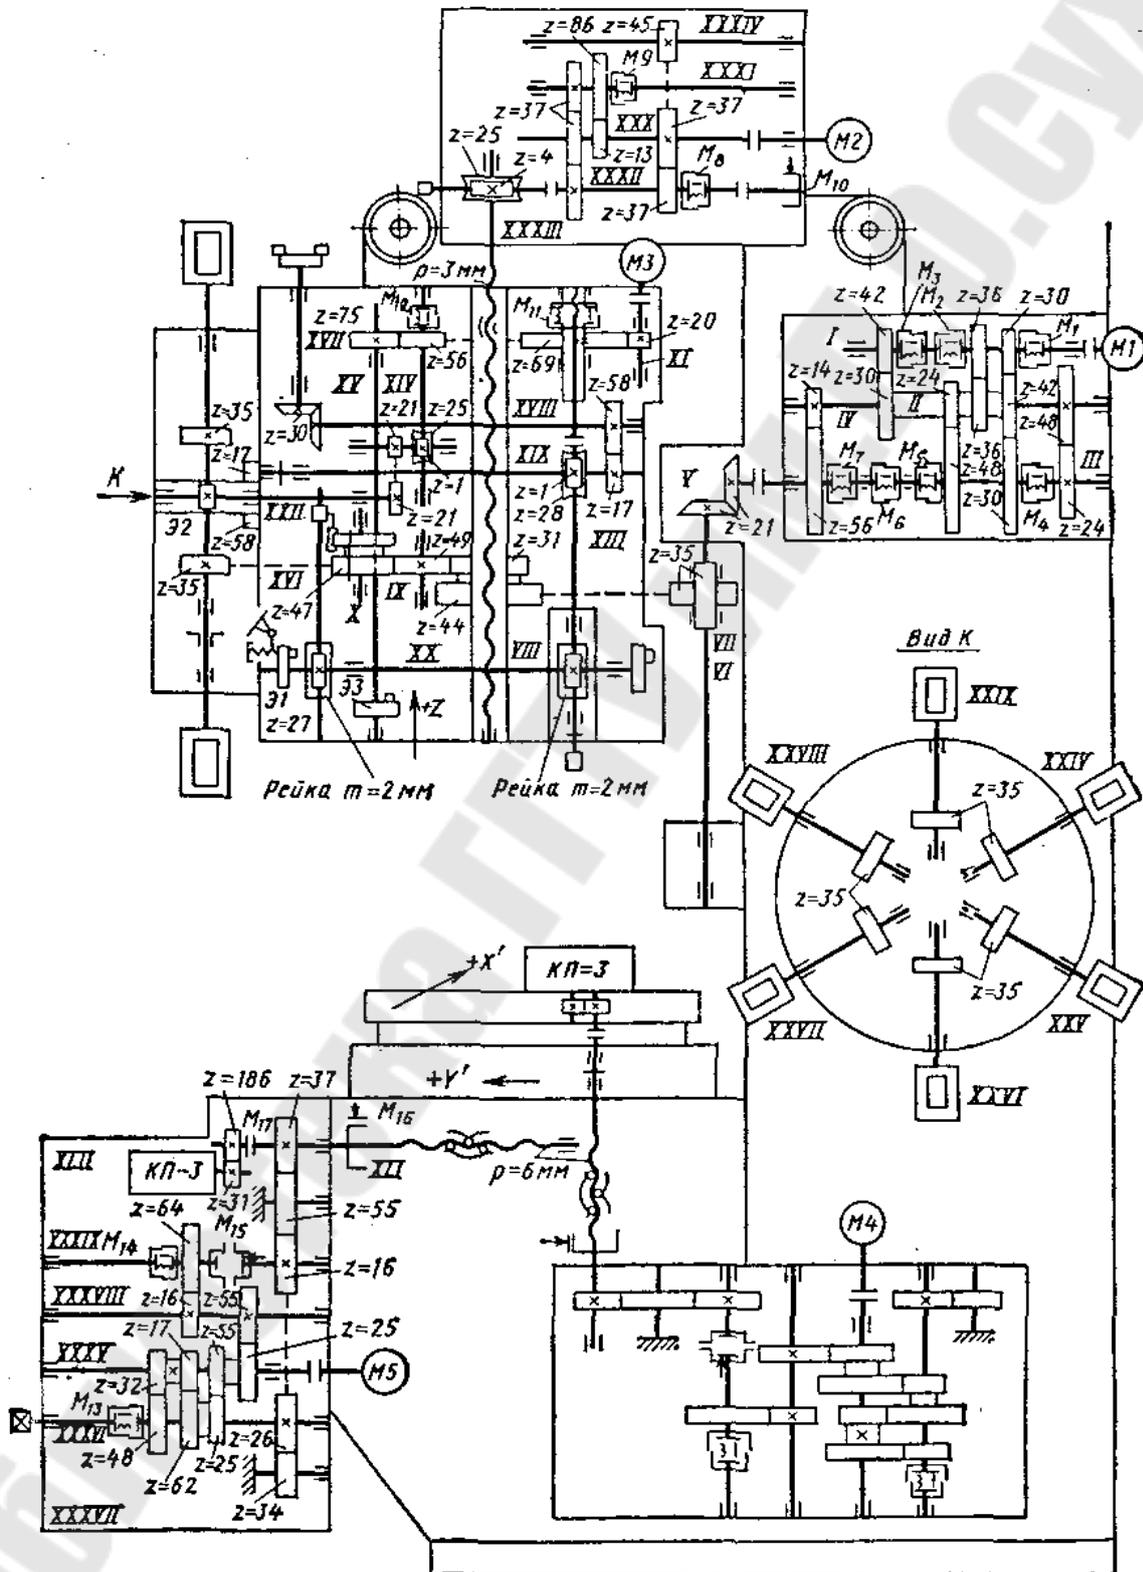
Кинематическая схема вертикально-сверлильного станка с ЧПУ
